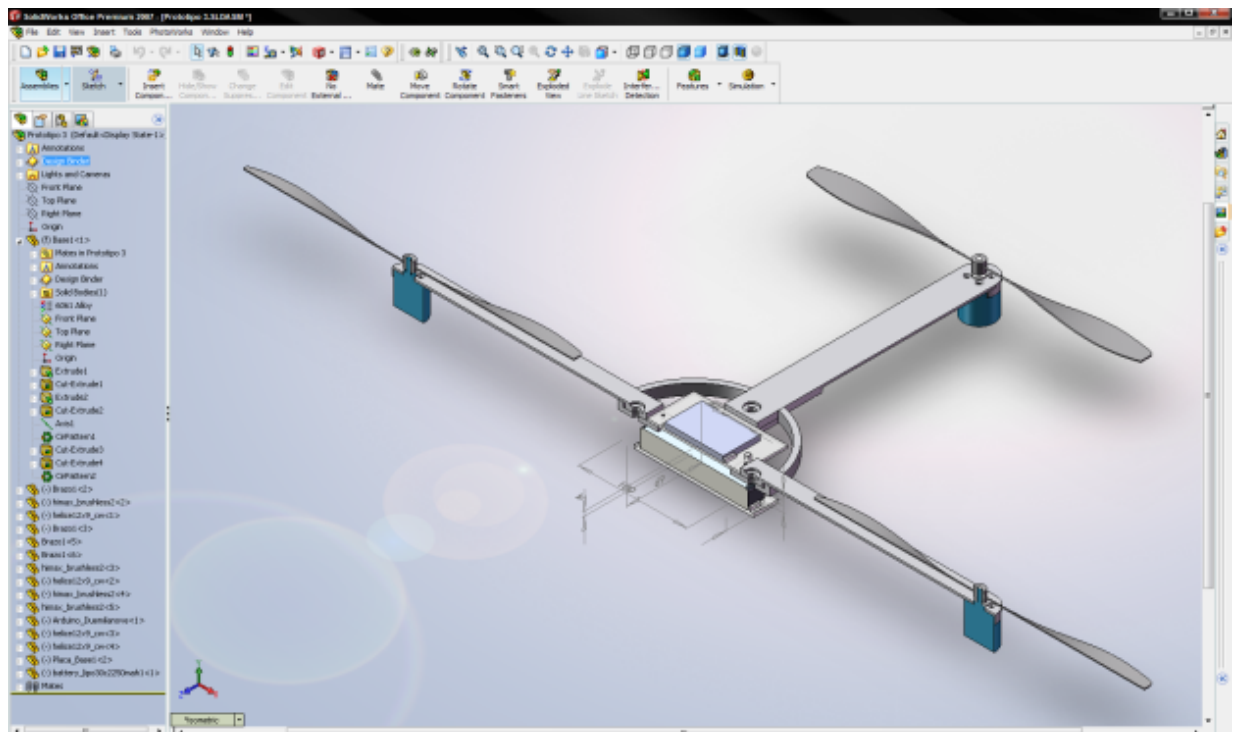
Prototipo 3 Solidworks – Vista en sección de ensamble.
